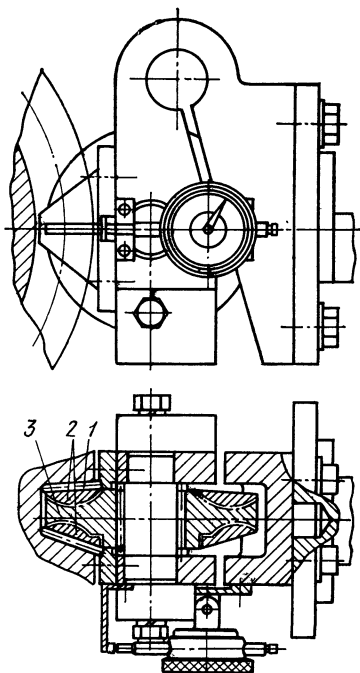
Устройство для обкатки упорной резьбы с шагом 64 мм:
